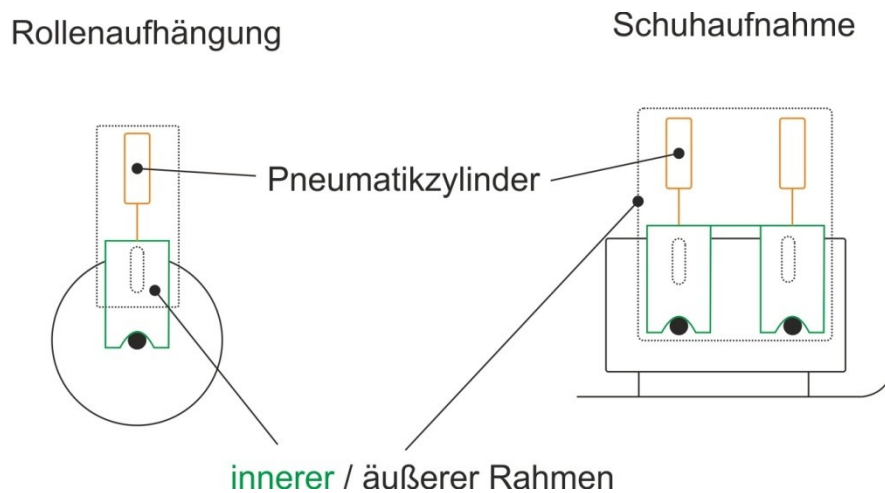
Konzeptvariante „Modul“ für die Ausführung des Konsolidierungssystems, links: Ein-Rollen Aufhängung, rechts: Zwei-Rollen bzw. Schuhaufhängung.
